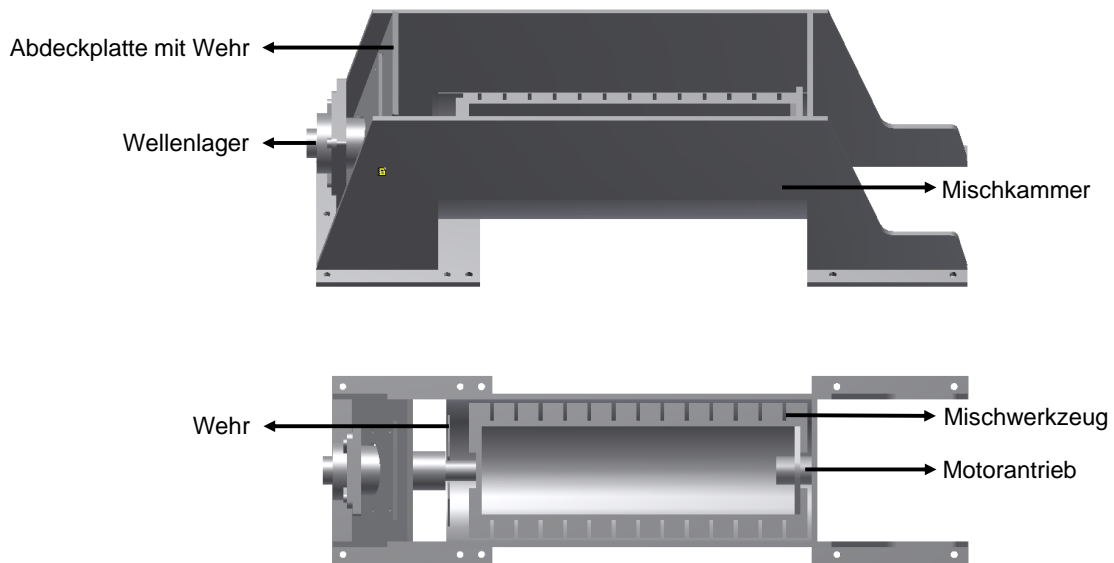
Mischkammer mit eingebautem Mischwerkzeug
